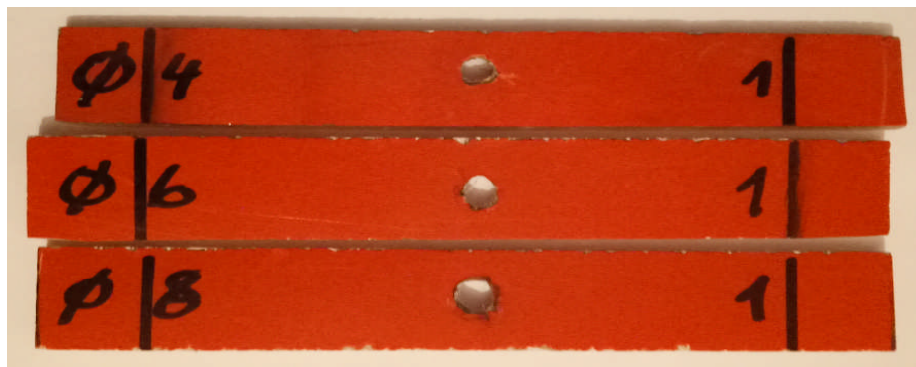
éprouvettes avec trous moulée (4, 6 et 8mm)
